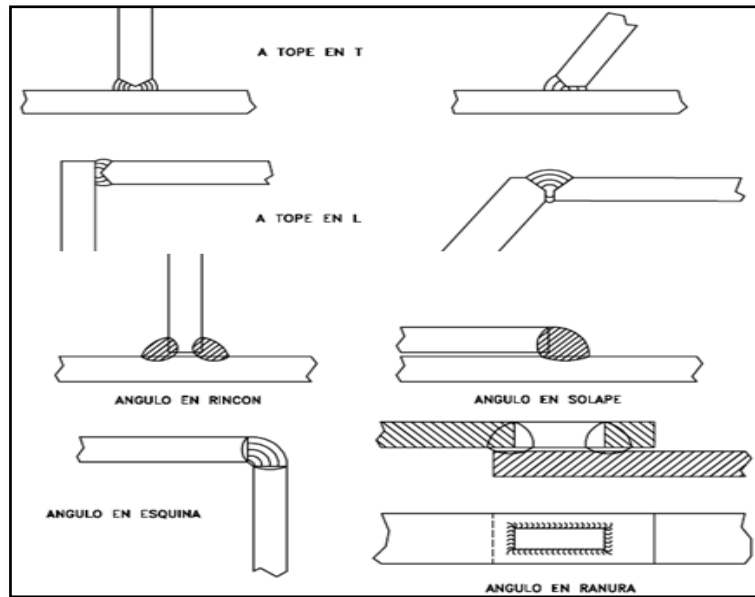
Cordón de soldadura a tope y en ángulo
